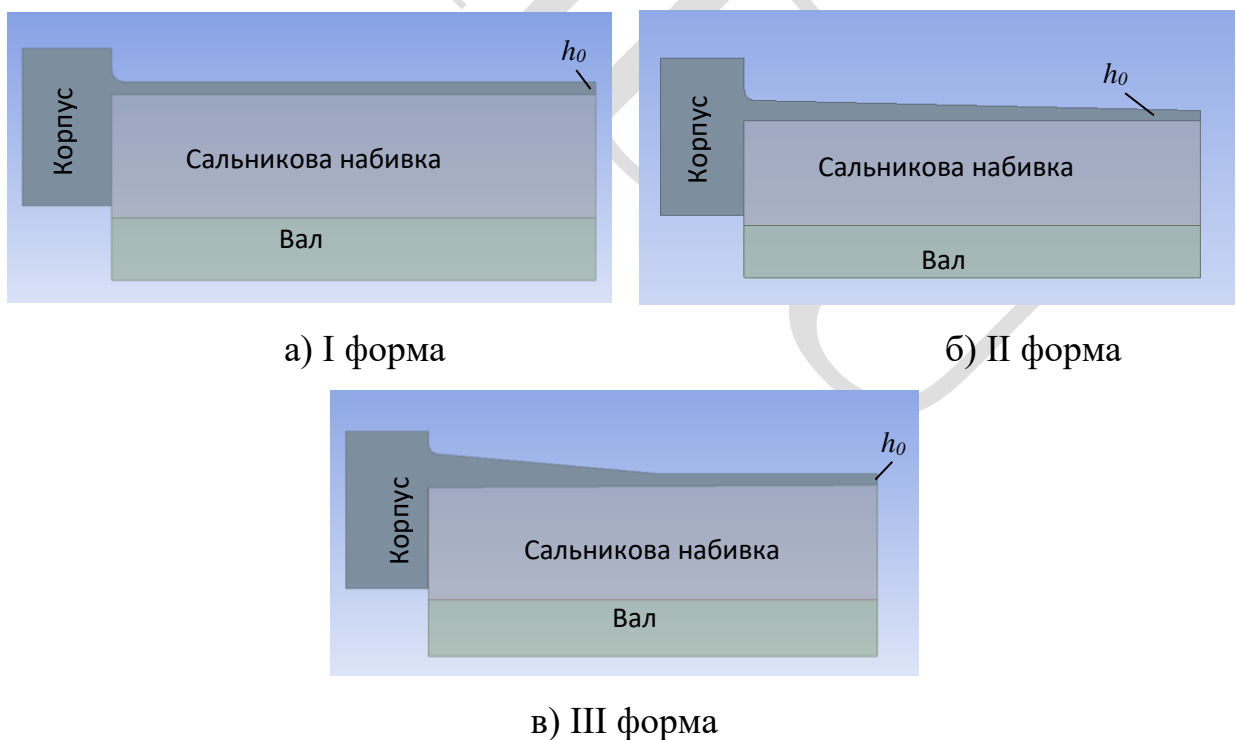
Сальникове ущільнення з різною формою деформованого корпусу
